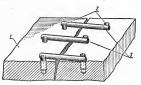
Подготовка толстостенной детали к заварке трещины:
